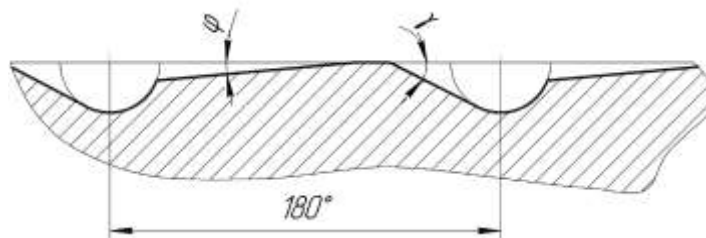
Розгортка торцевої поверхні ведучої півмуфти
